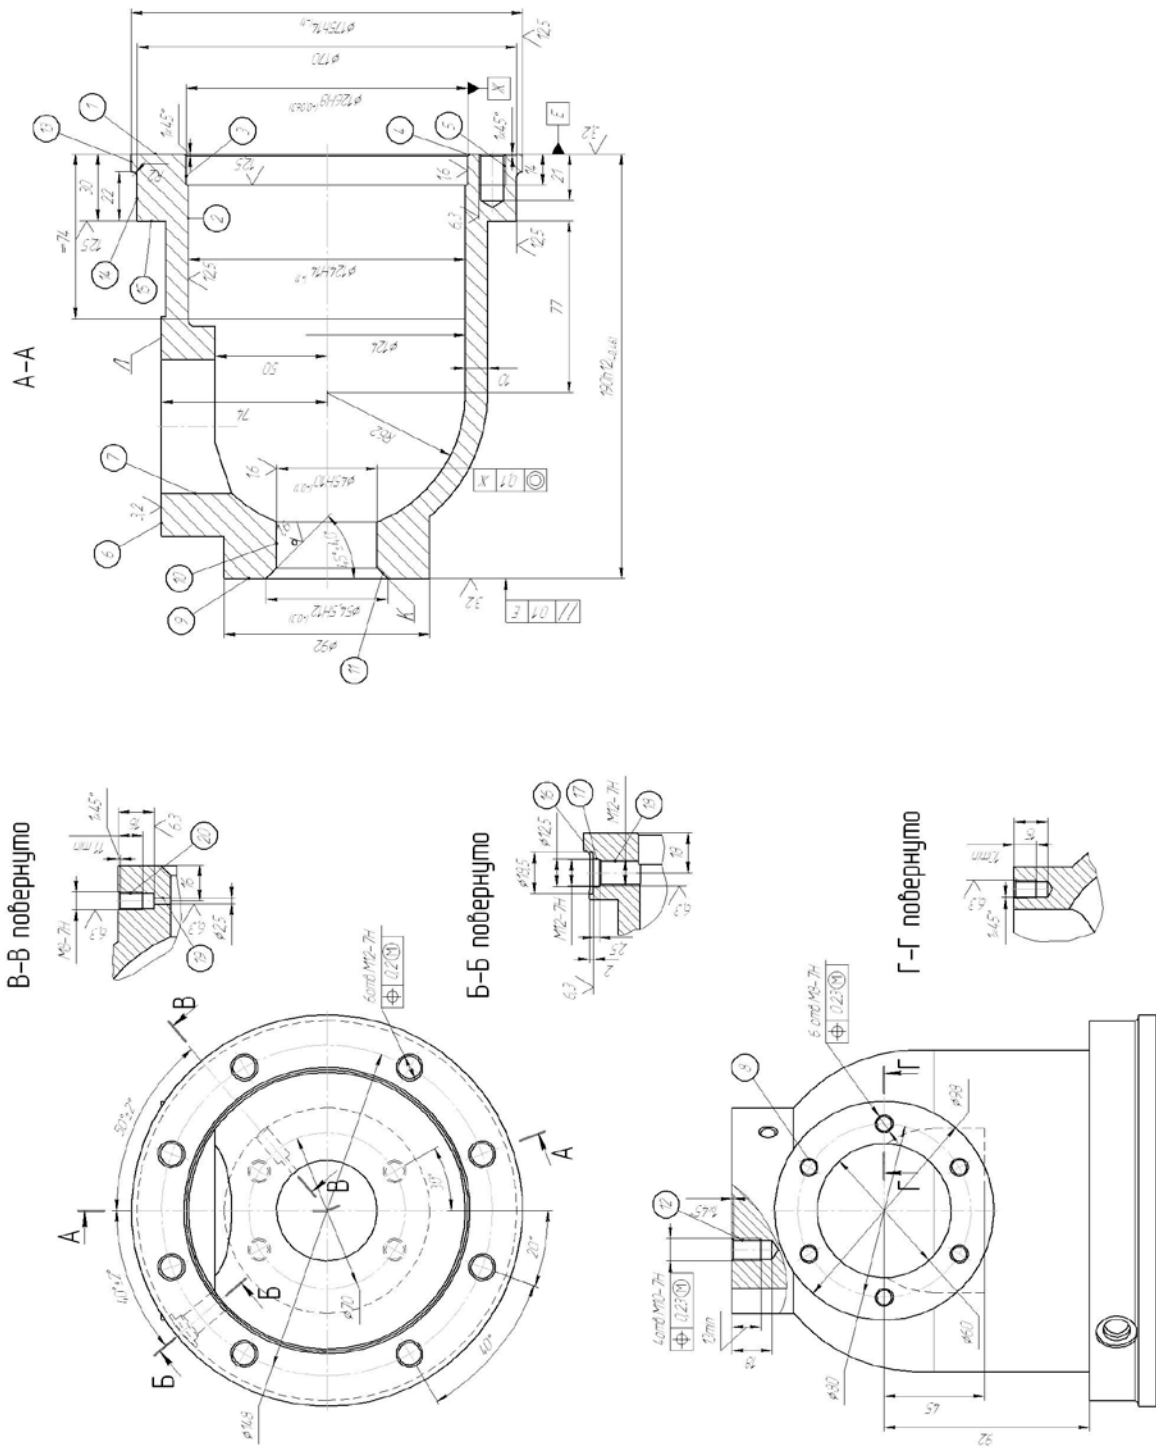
Нумерація поверхонь деталі – Корпус ДГК 10.030.20
